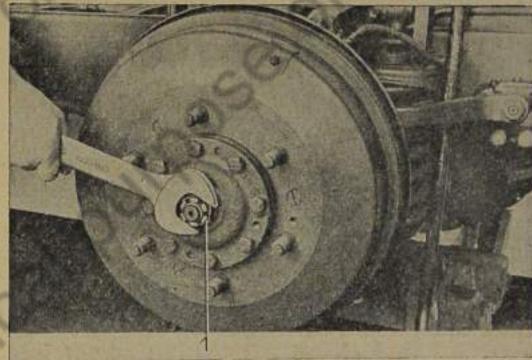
Kronenmutter von Quergelenkwelle abschrauben
